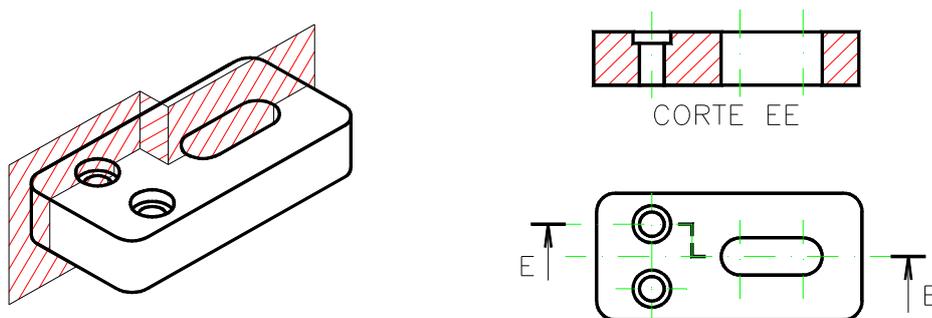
corte longitudinal de uma peça com elementos iguais alinhados em um plano transversal.
